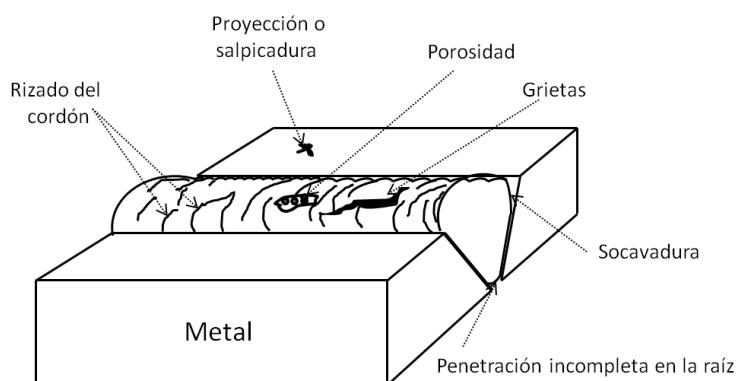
Fuentes de resquicios en la zona de soldadura
